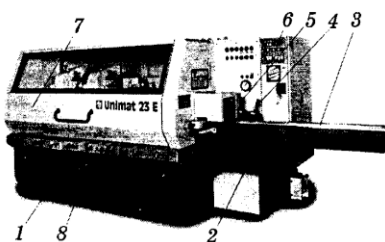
Загальний вигляд середнього чотирибічного поздовжньо-фрезувального верстата: 1 — станина; 2 — передній стіл; 3 — напрямна лінійка; 4 — ручка налагодження положення переднього стола; 5 — ручка налагодження положення напрямної лінійки; 6 — пульт керування; 7 — звукопоглинаюче огородження; 8 — елементи розмірного настроювання ножових головок
